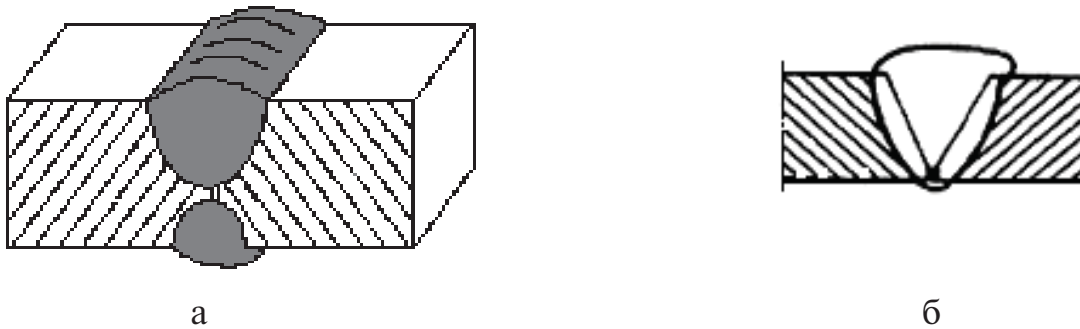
Схематичное изображение неправильного профиля сварного шва:
